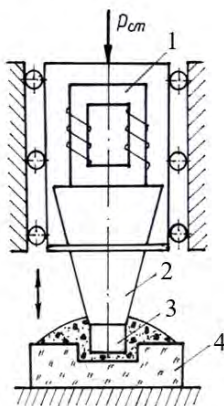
Схема ультразвуковой размерной обработки: 1 – преобразователь; 2 – стержневой концентратор; 3 – инструмент; 4 – заготовка
